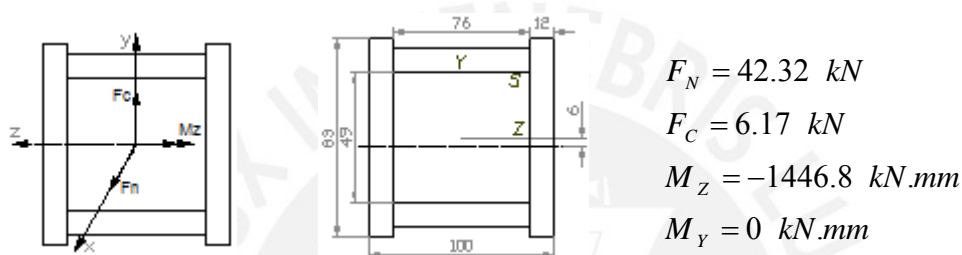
Sección transversal en Primer Cambio de Sección.
